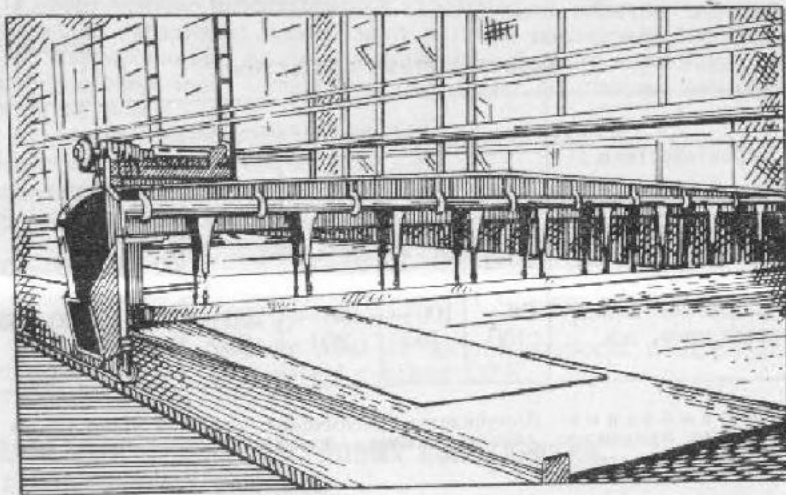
Стенд с прижимной балкой для сварочных работ.
